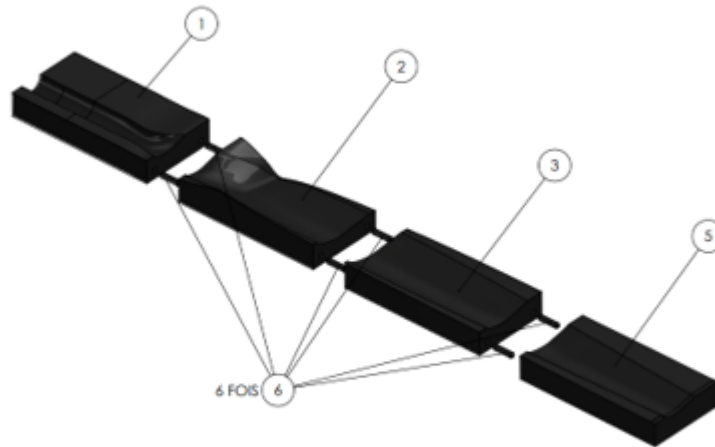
Vue éclatée des composants de la partie supérieure du moule
